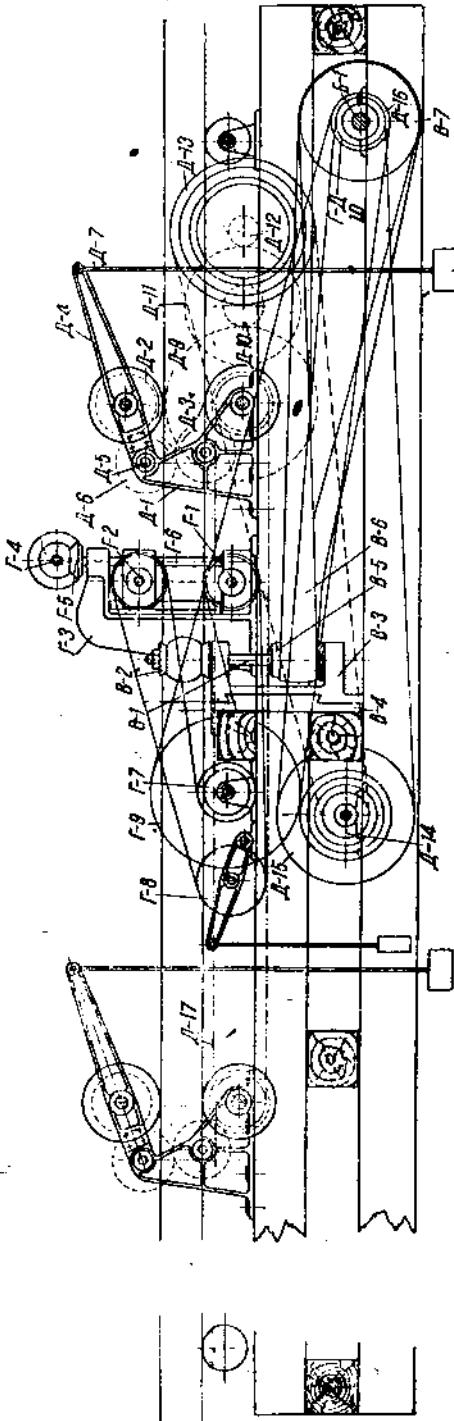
Четырехсторонний универсальный строгальный станок для профилировки стен и других тяжелых полуфабрикатов
